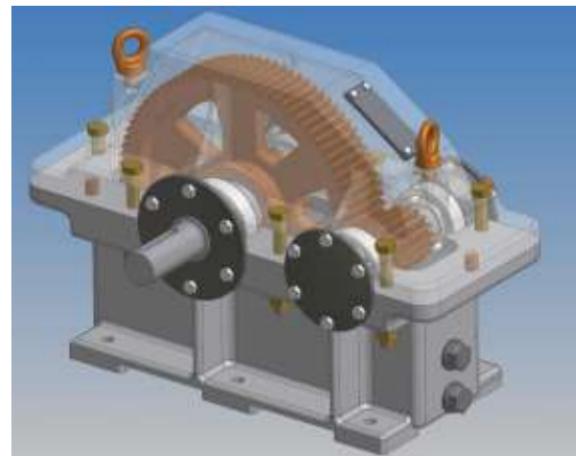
Загальний вид горизонтального двоступеневого редуктора
